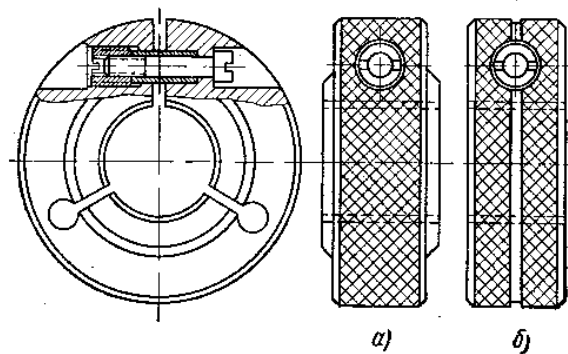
Резьбовые калибры-кольца: а — проходные, б — непроходные
